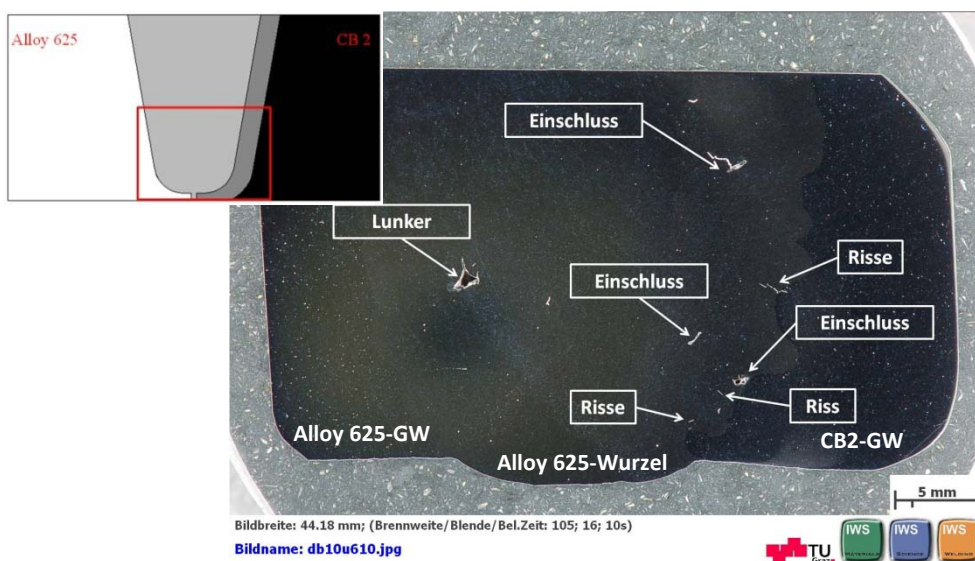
Schweißfehler im Massivdraht-Schweißgut; Massivdrahtelektrode, (3.Probe), nicht geätzter Zustand.
